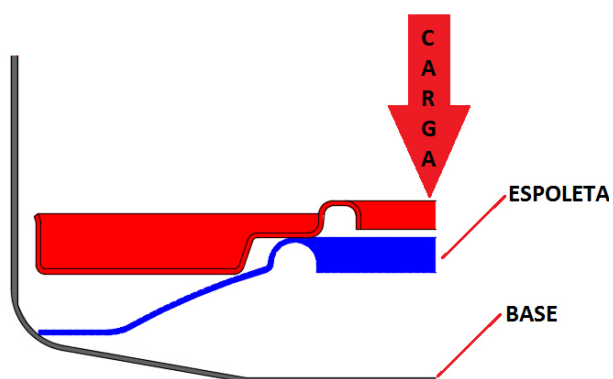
Esquema de montaje de la espoleta durante la prueba mecánica.
